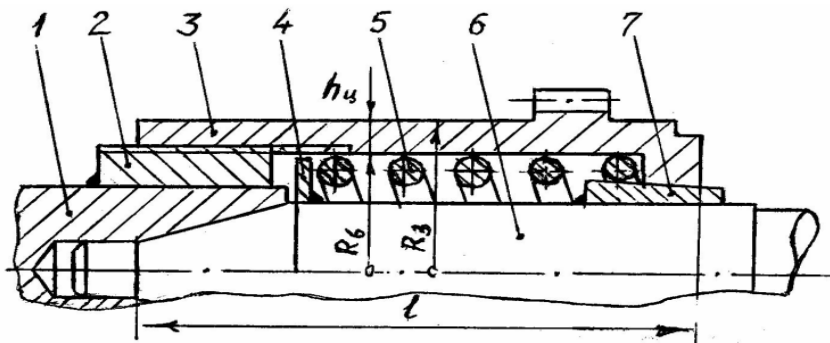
Конструктивна схема ЗЗЖ: 1 – вал вхідний; 2 – втулка регулювальна; 3 – стакан; 4 – шайба; 5 – пружина; 6 – вал вихідний; 7 – конусна втулка
